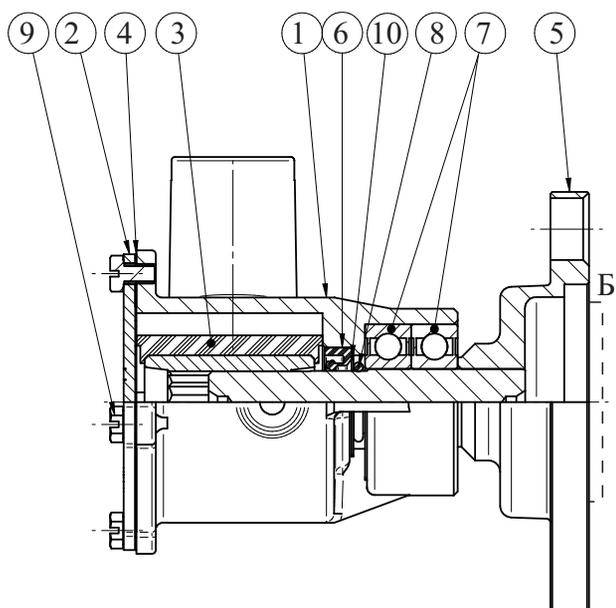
Насос Johnson Pump. 1 – корпус, 2 – крышка, 3 – крыльчатка, 4 – прокладка, 5 – фланец в сборе с валом, 6 – сальник, 7 – подшипники 6203, 8 – кольцо стопорное, 9 – винты крепления крышки, 10 – шайба
